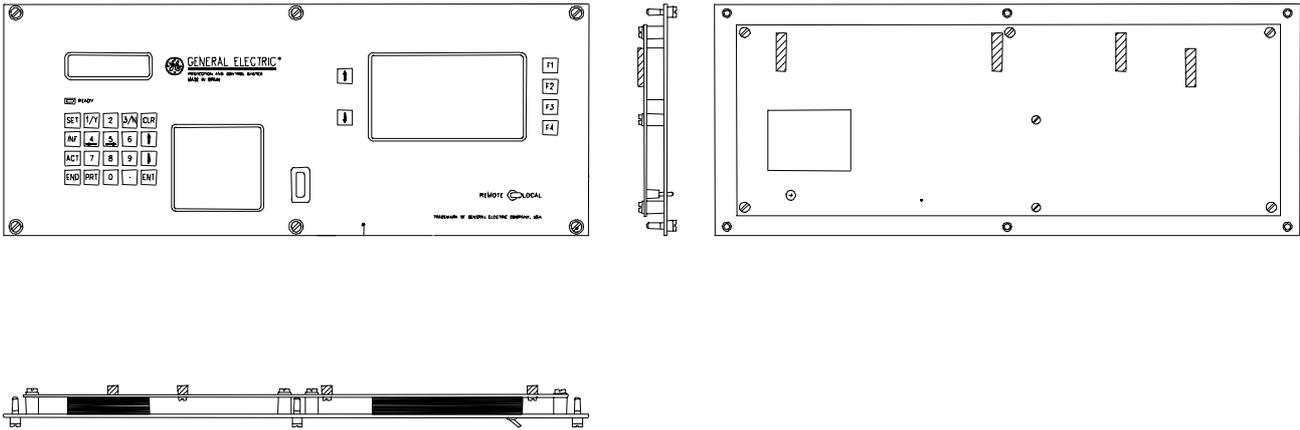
Ensemble partie frontale (226B3351 Fig. 1)
